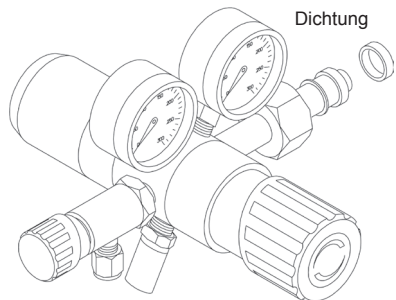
Flaschendruckminderer mit Dichtung für Flaschenanschluß
